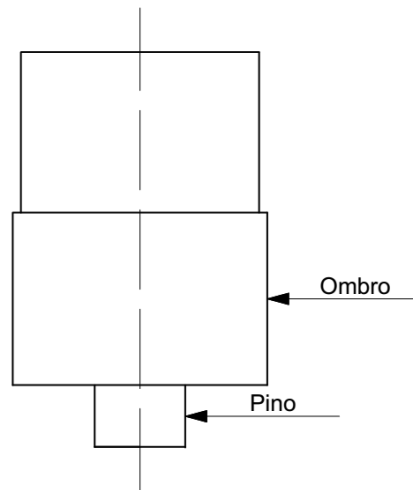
Componentes da Ferramenta de Soldagem FSW [Autor].
